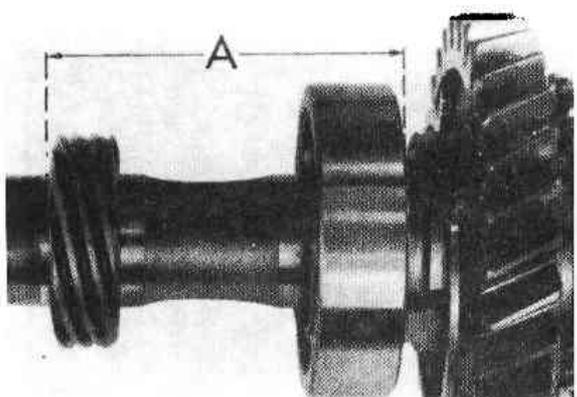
Размещение шестерни привода спидометра коробки передач типа В (Разд.6)
